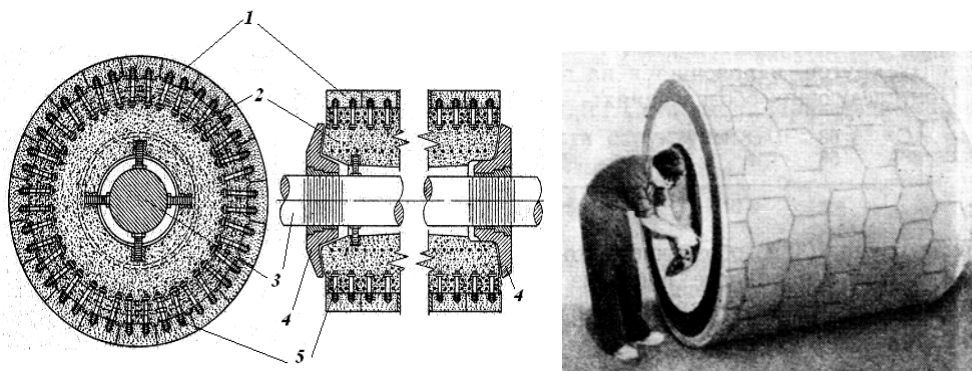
Внешний вид и устройство керамического дефибрерного камня и его крепление к валу дефибрера:
